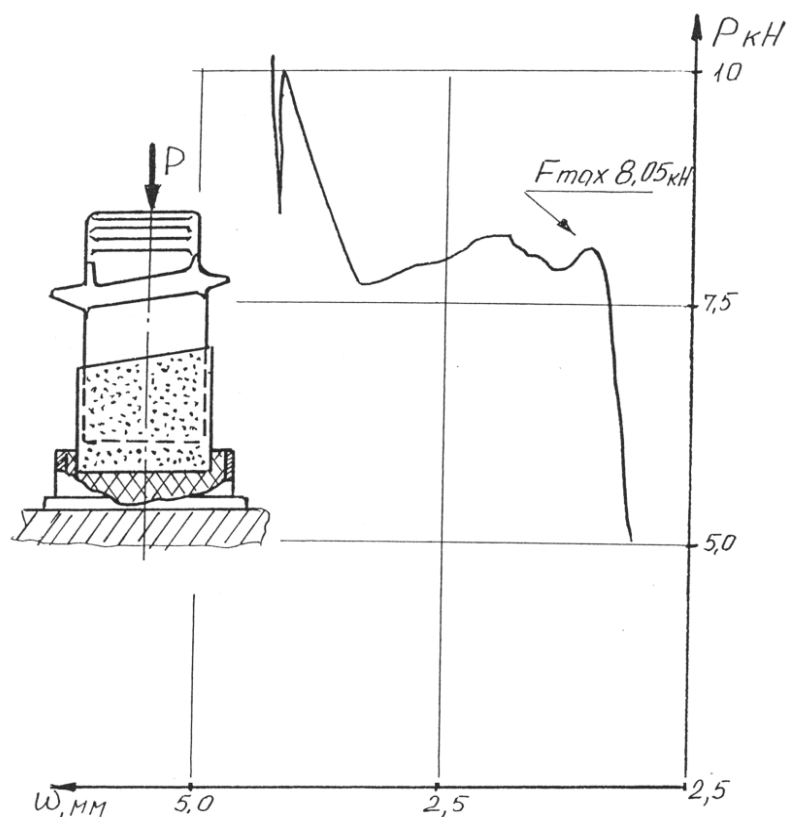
Испытание на сдвиг сварного соединения оболочки со стержнем турбинной лопатки
